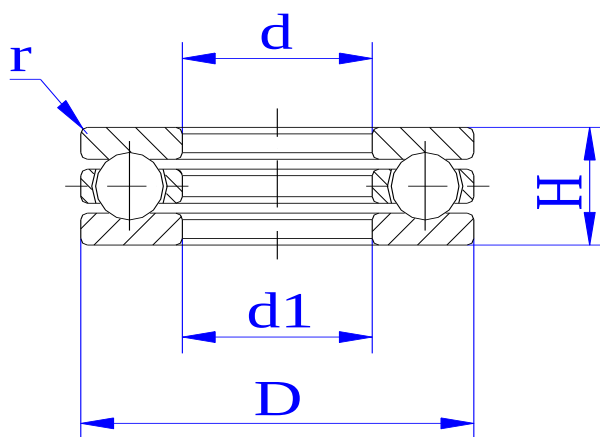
Ескіз кулькового упорного підшипника 8103
